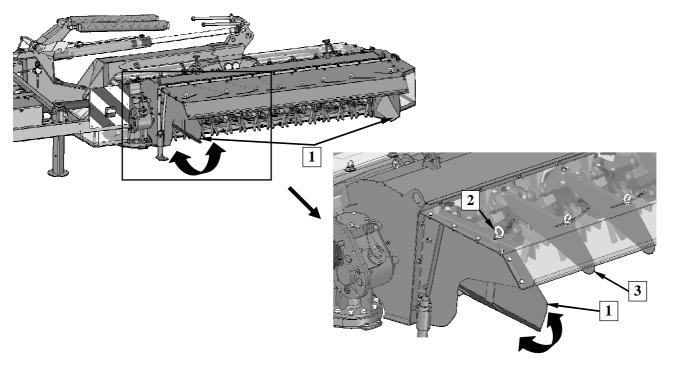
Regulierung der Schwadformer: 1-Schwadformer, 2-Regelschraube, 3- Schwadlenker
